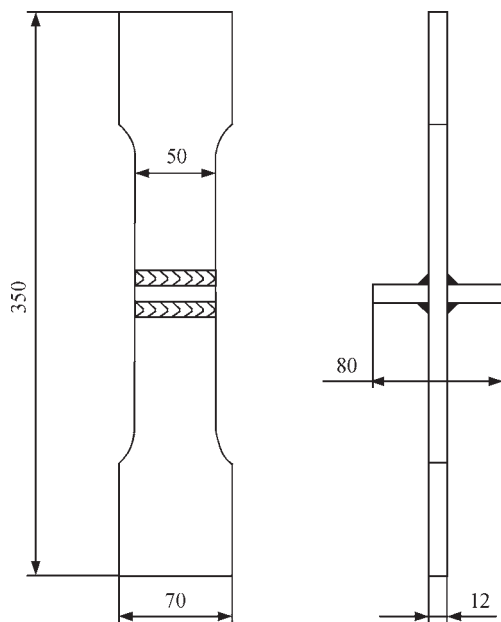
Форма та геометричні розміри зразків таврового зварного з'єднання
